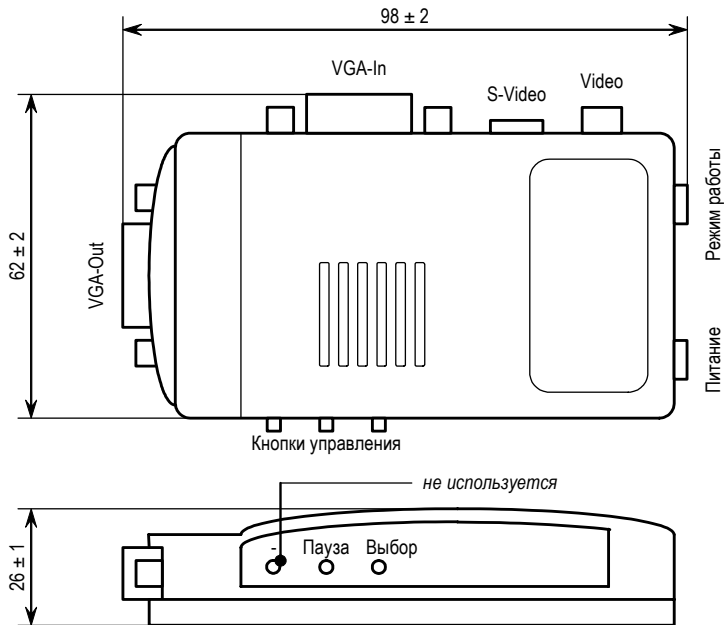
Габаритный чертеж преобразователя TV-VGA
